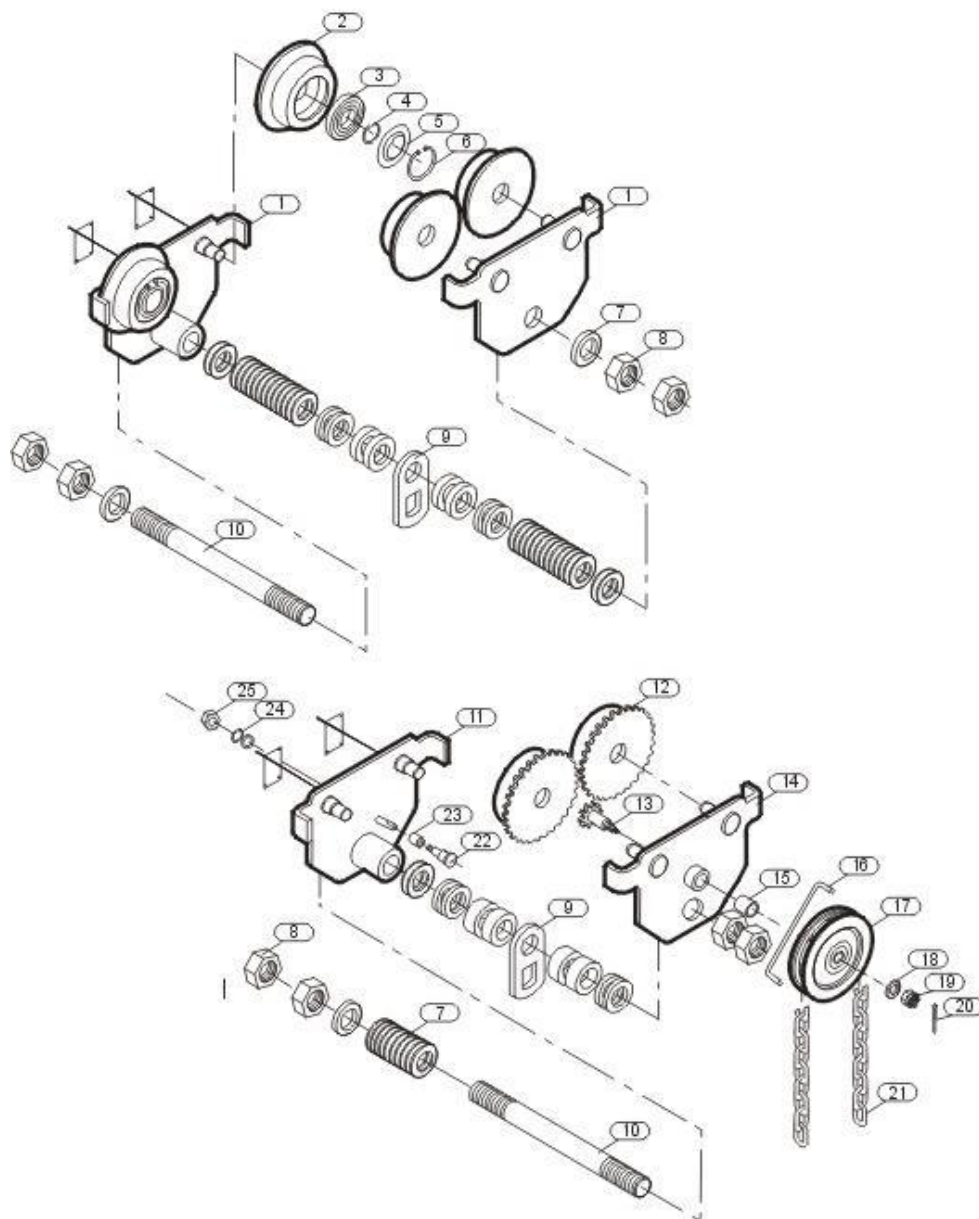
Взрыв схема тележки приводной для тали GCL.
